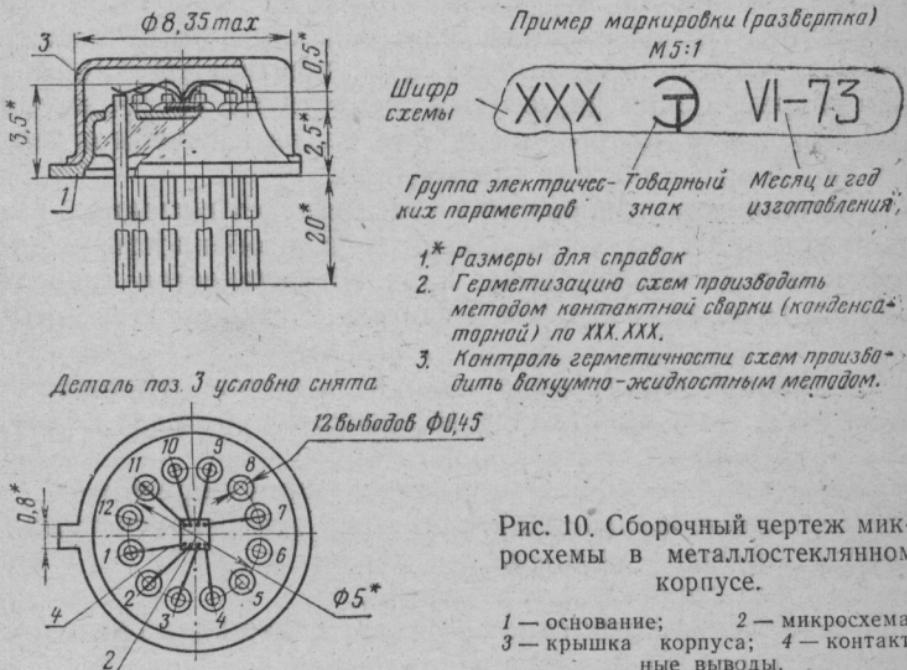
Сборочный чертеж микросхемы в металлостеклянном корпусе.
